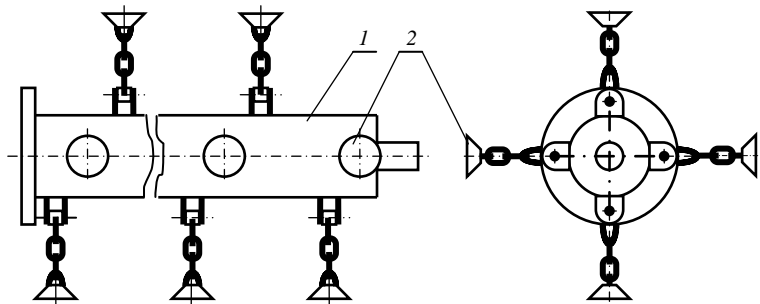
Схема ротора косилки-измельчителя с шарнирно закрепленными чашечными ножами: 1 – барабан; 2 – ножи
